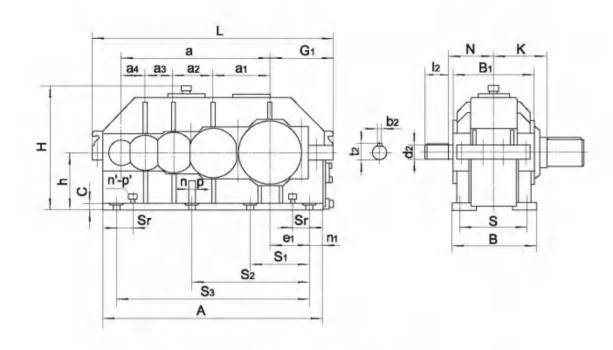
QY4D减速器外形尺寸 Figure 10 External dimension of QY4D decelerator
